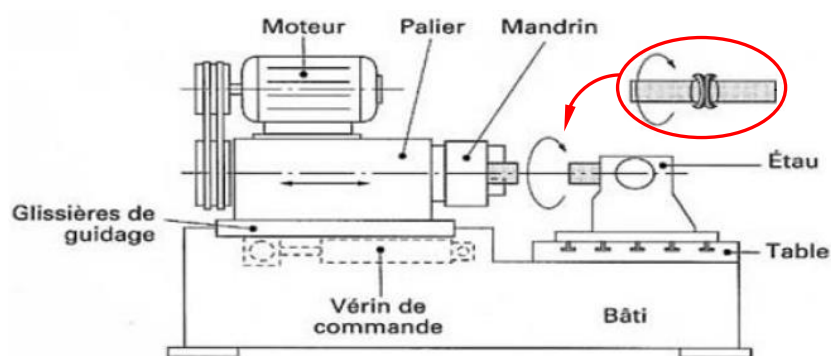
Schéma d'une machine de soudage par friction
